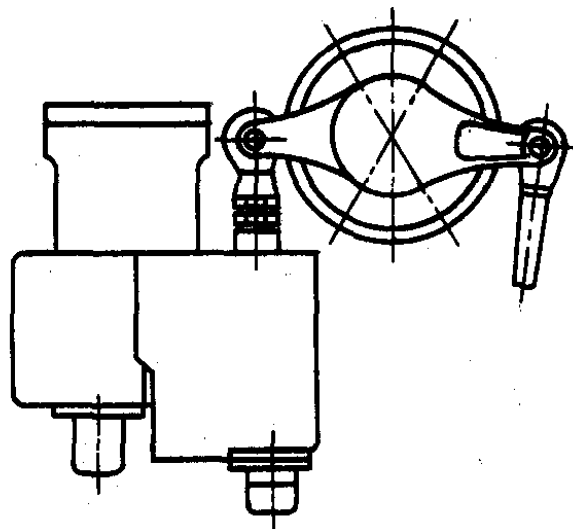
Установка рулевой машинки на подвижном ушке вала
